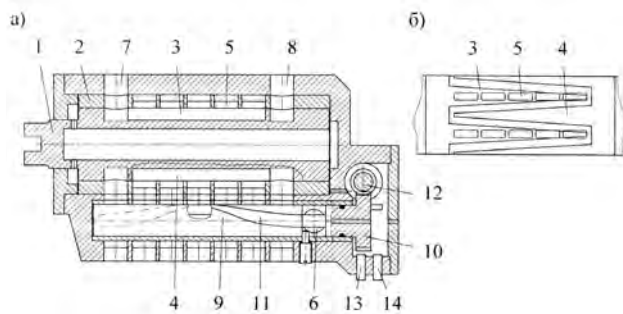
ДГ с регулированием параметров потоков: а — продольный разрез, б — развертка ротора; 1 — ротор, 2 — статор, 3, 4, 5 — продольный канал, 6, 7, 8 — каналы корпуса ДГ
